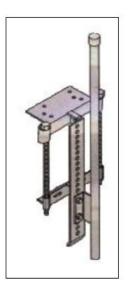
Elevador de un poste. www.hydrohoistmexico.com/partesyaccs.htm
